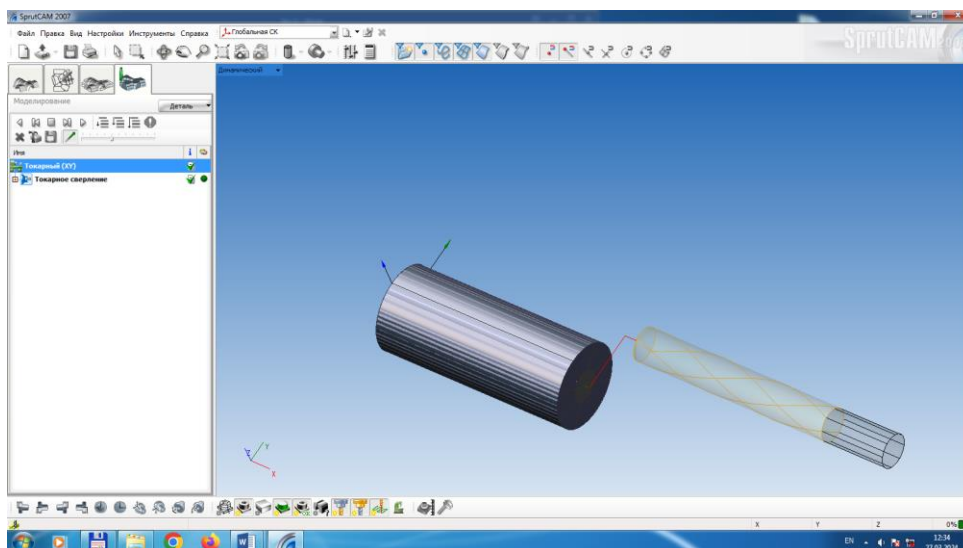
Інструмент і заготовка перед початком свердління
